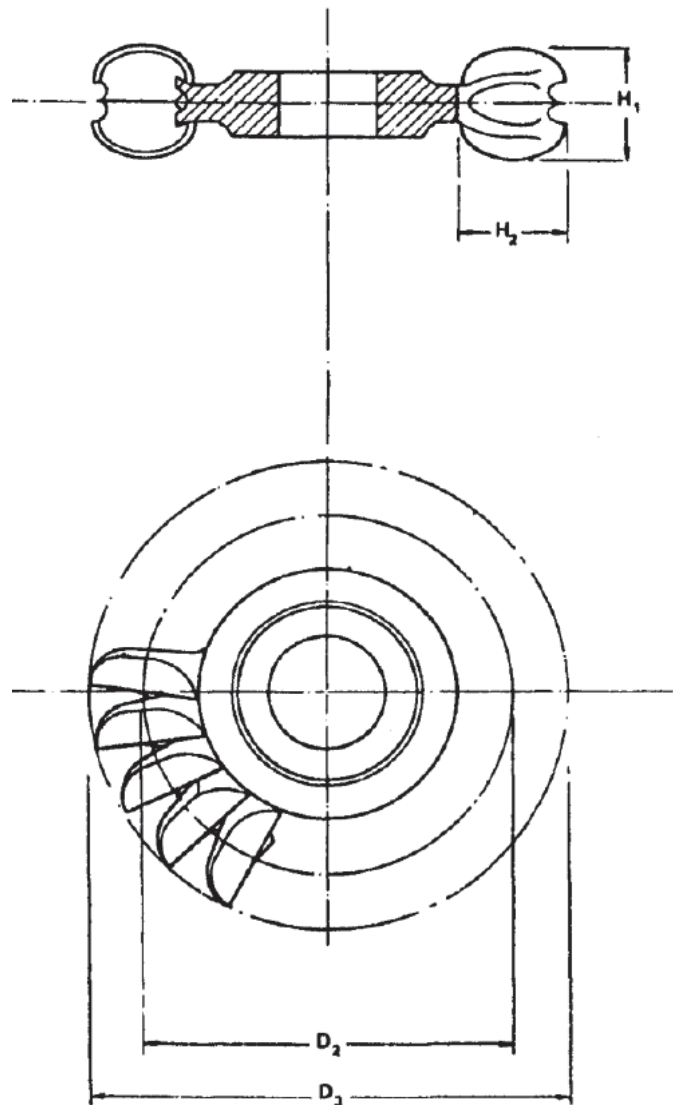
Turbina Pelton: Dimensiones del Rodete
